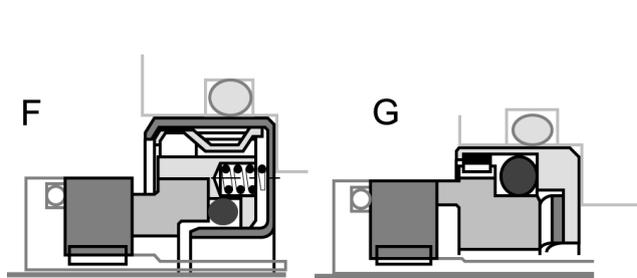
Kleinbauende GLRD mit stationärem Gleitring
